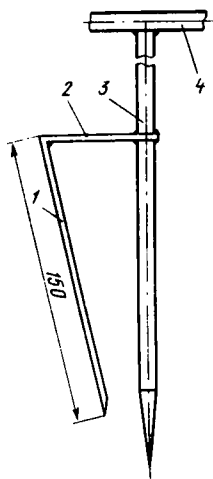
Устройство с изогнутым ножом для удаления корневищ из почвы: 1 — нож; 2 — консоль; 3 — стержень; 4 — рукоятка
